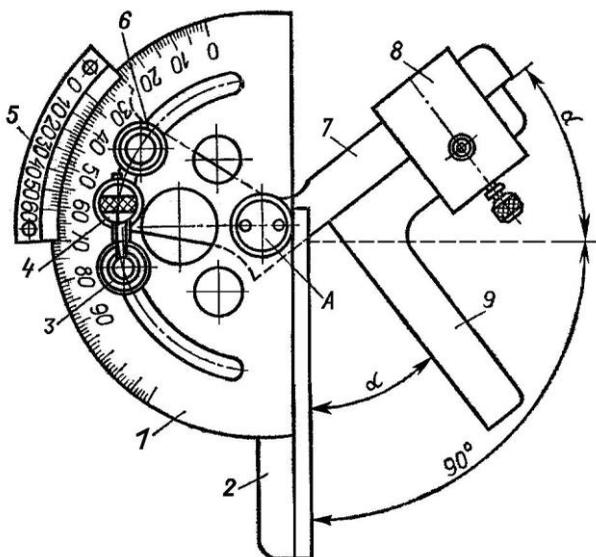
Угломер транспортирный с нониусом конструкции Кушникова
